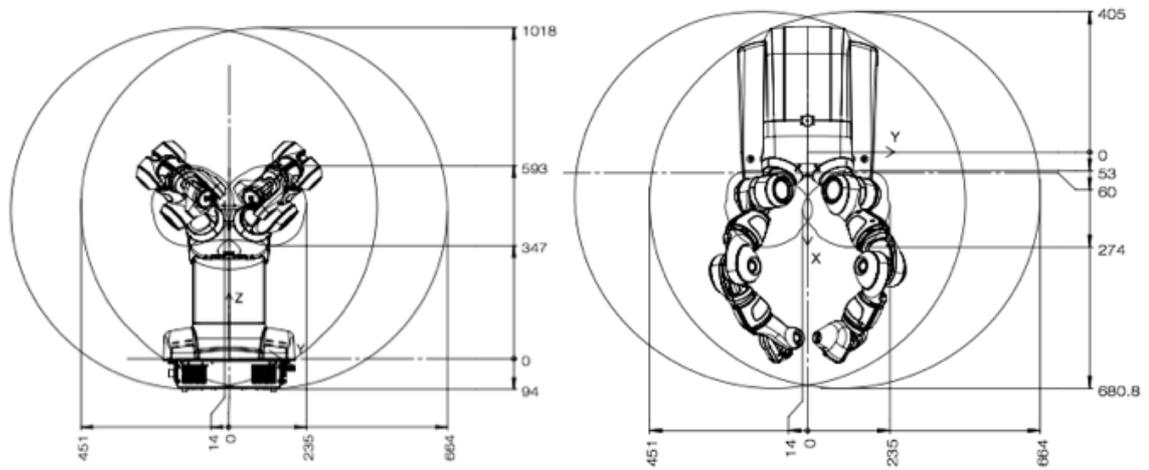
Spazio di lavoro (dimensioni in mm)
